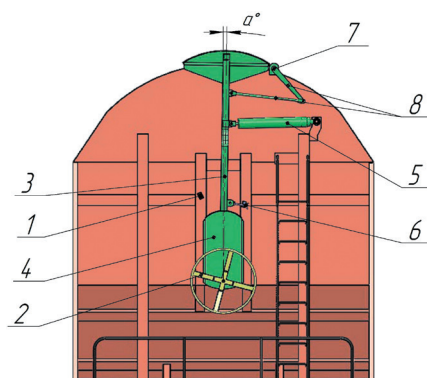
Расположение основных элементов конструкции: 1 — упор; 2 — штурвал; 3 — поворотная стойка; 4 — защитный кожух; 5 — амортизатор; 6 — фиксатор; 7 — торсионный вал; 8 — рычаги торсионного вала
